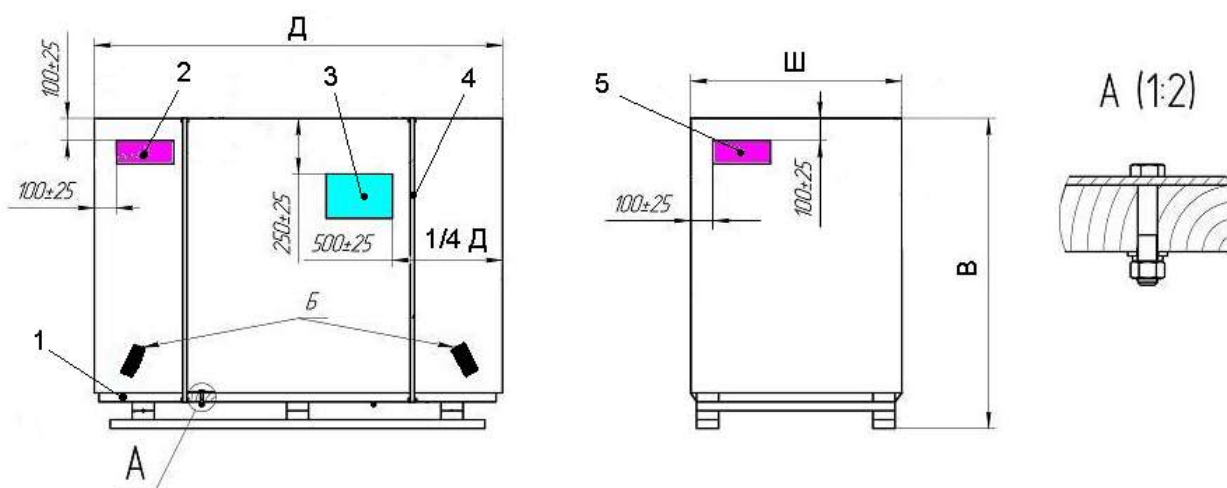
Упаковочный гофроящик установки: 1 – поддон; 2 и 5 – наклейки «Манипуляционные знаки»; 3 – наклейка «Транспортная маркировка»; 4 – клеевая лента; Б – наклейка «Места строповки».
